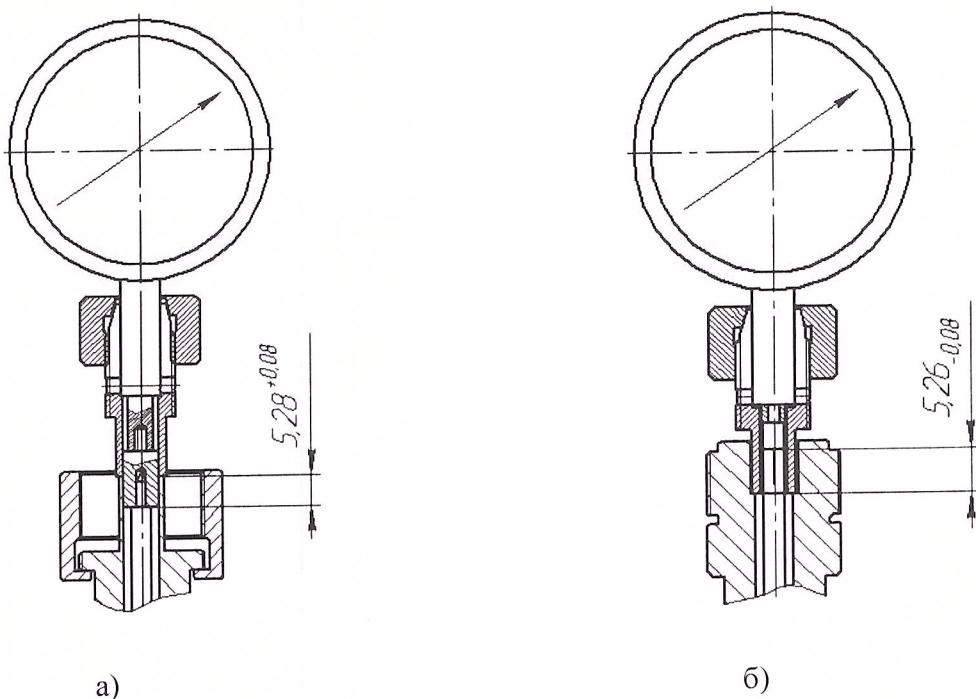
Схема измерения а) для размера  $5,28^{+0,08}$  б) для размера  $5,26^{-0,08}$
